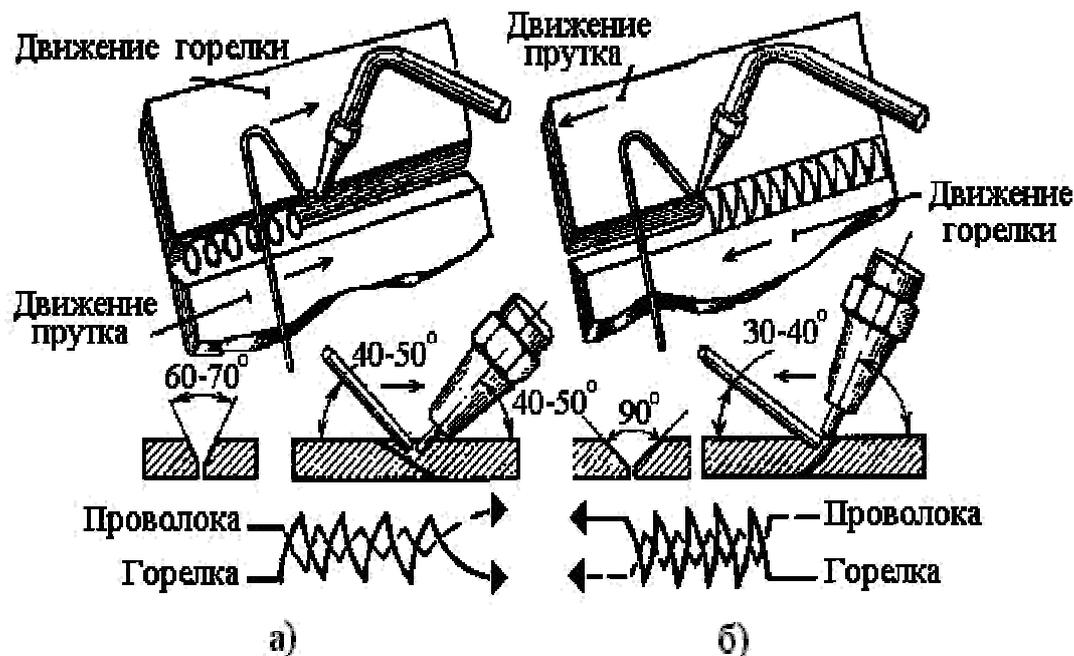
Способы газовой сварки: а- левый; б – правый.
